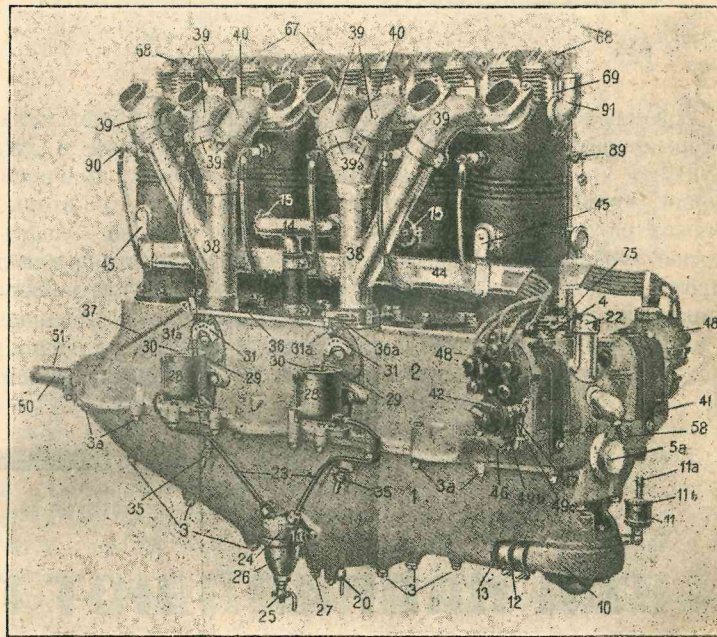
150-сильный двигатель „Бенц“ (вид со стороны карбюраторов).
